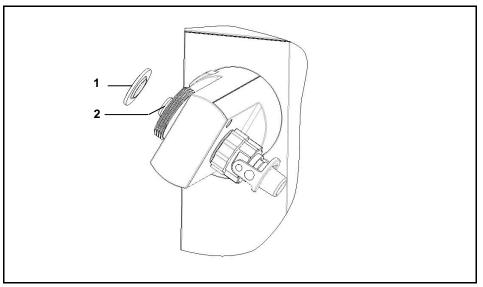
Pose du joint en PTFE sur le conduit de vapeur
